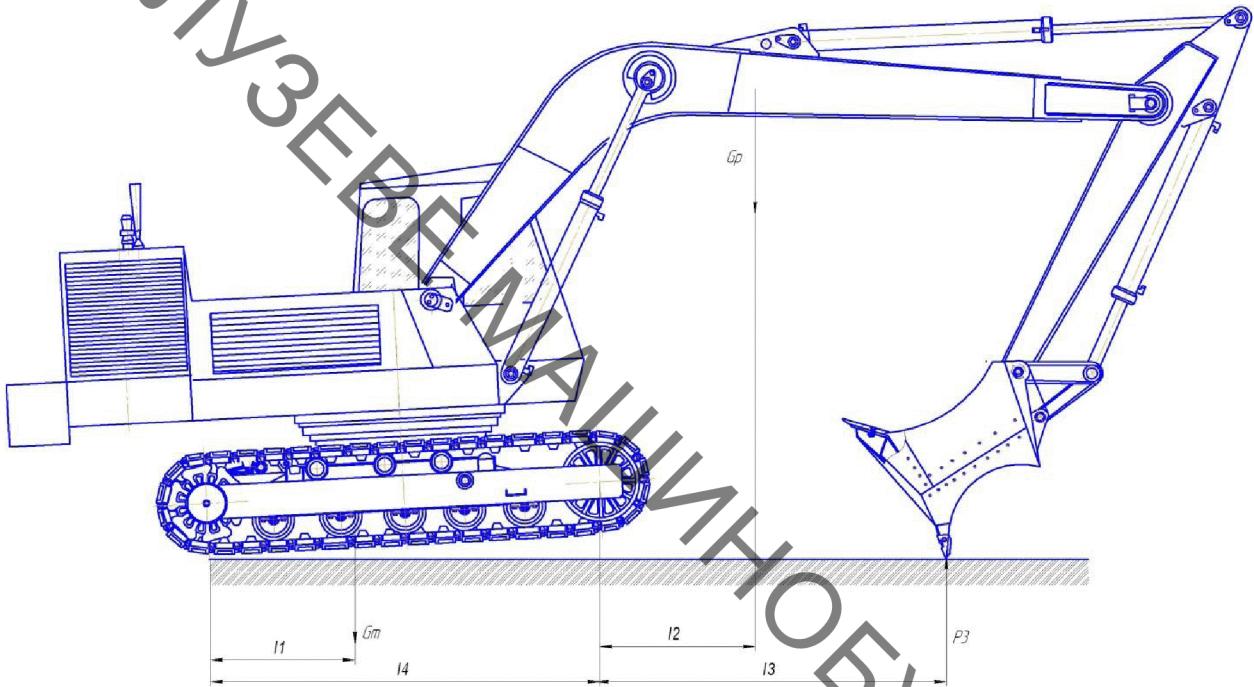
Схема для визначення зусиль заглиблення зубів розпушувача
